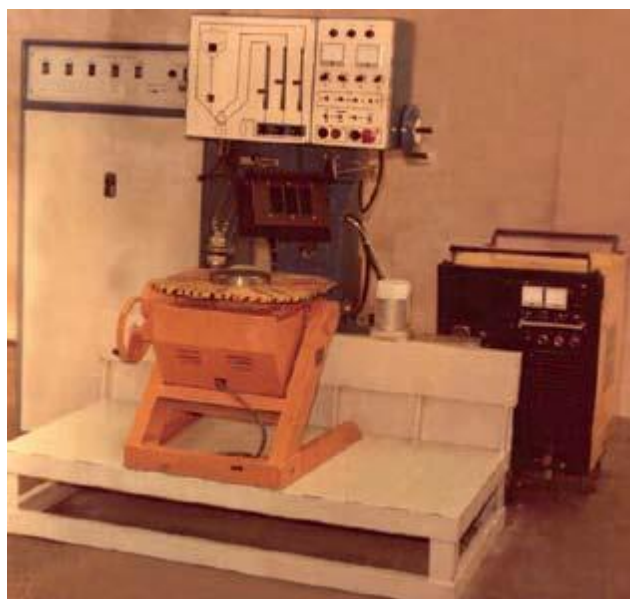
Универсальная установка для плазменной наплавки ОБ-2184
